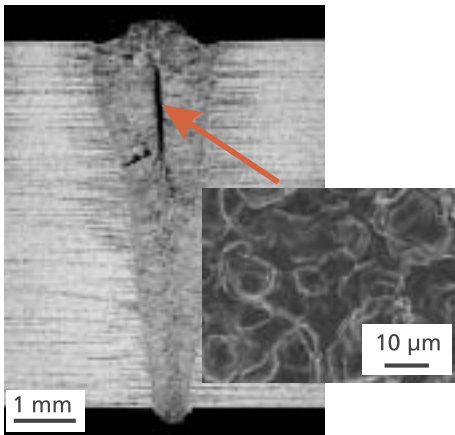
Schweißnaht nach herkömmlichem Laserstrahlschweißen, Detail: REM-Aufnahme der Oberfläche des Erstarungsrisse, freigelegt durch Ermüdungsbruch senkrecht zur Schlifffebene
